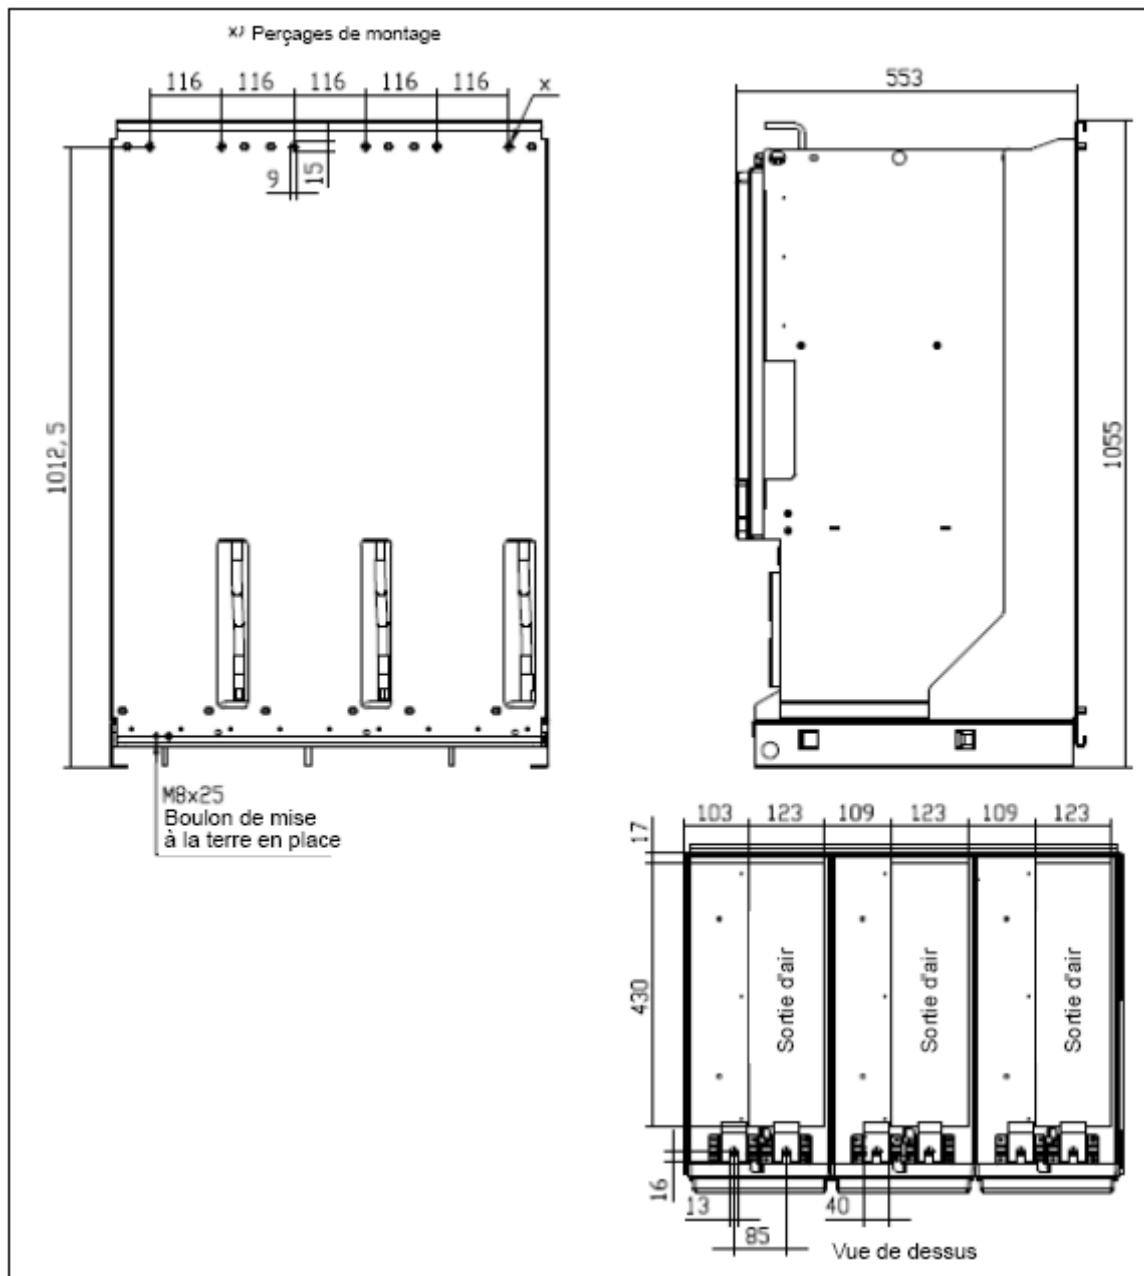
Dimensions du Vacon NXI, F113 (face arrière). Nota : F114 est constitué de deux F113.
